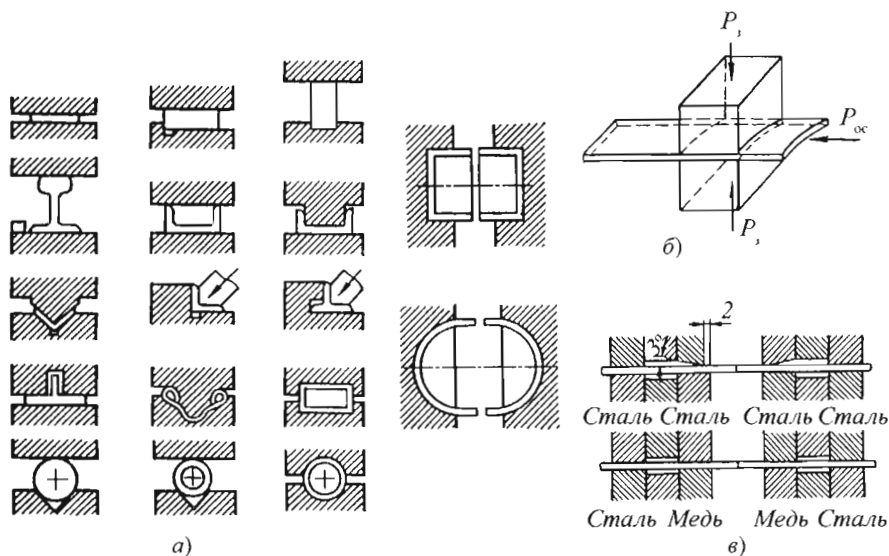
Электроды (сварочные губки) для стыковой сварки заготовок разной формы сечения (а) и тонких полос (б, в):
